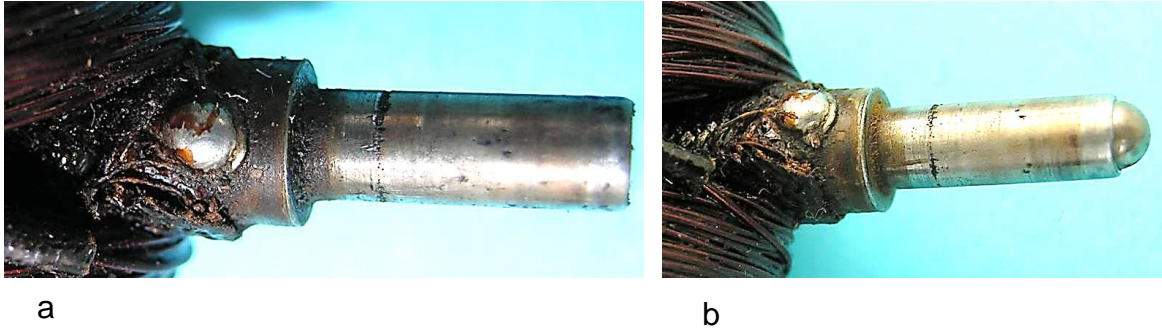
Wellenende mit Massekontakt: a) Ohne Kugel, b) Mit Kugel des Axiallagers
